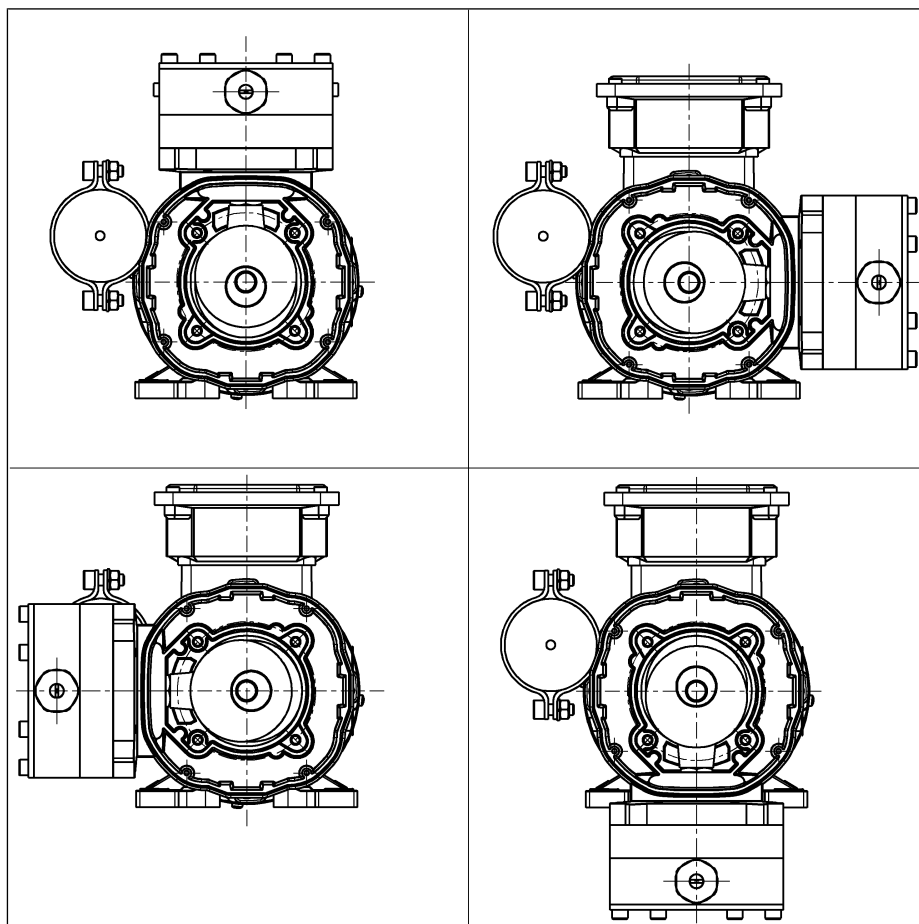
Posiciones de montaje de la carcasa de la bomba (bomba mostrada N922FT.29E)
